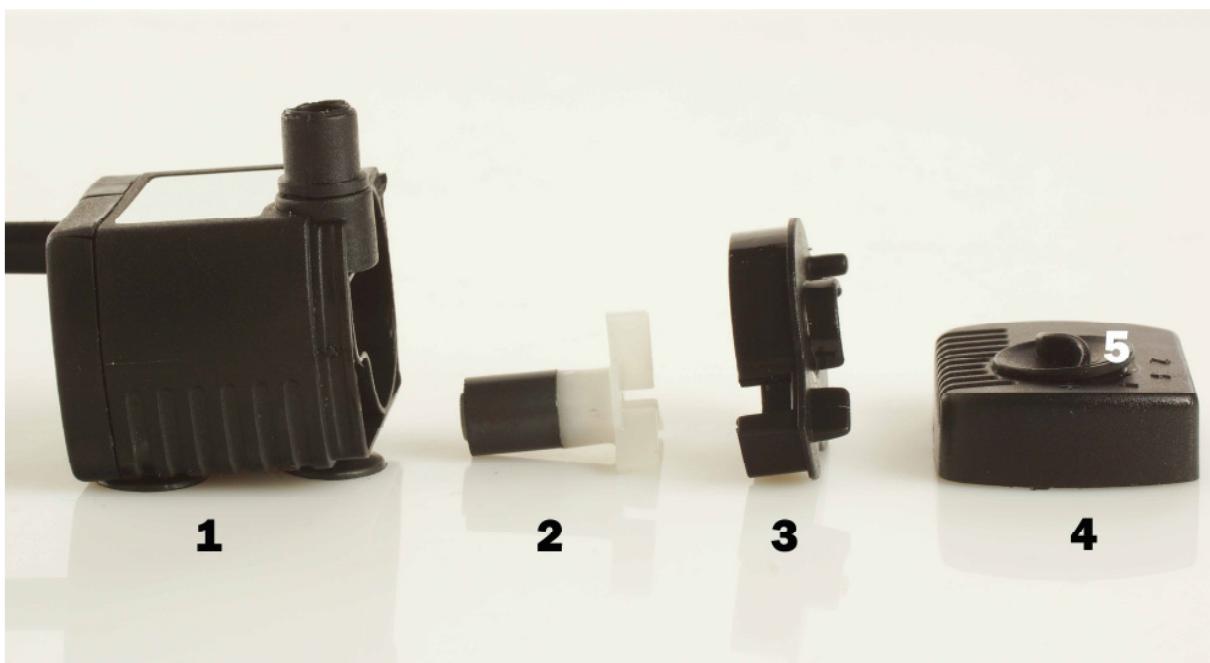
Reaktor S - 1. Pumpe 2. Impeller 3. Verschluss Kreiselgehäuse 4. Pumpenkorb
